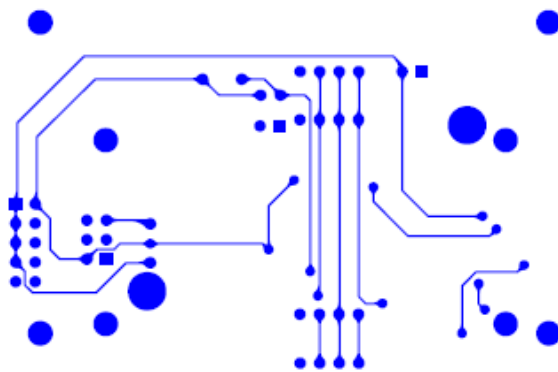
Layout* de la capa inferior del PCB a tamaño real
